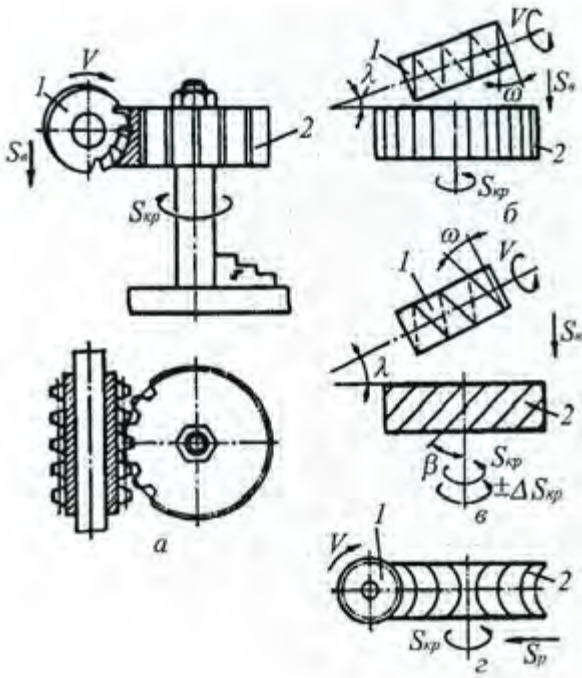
Схеми нарізування циліндричних зубчастих коліс на зубофрезерному верстаті
